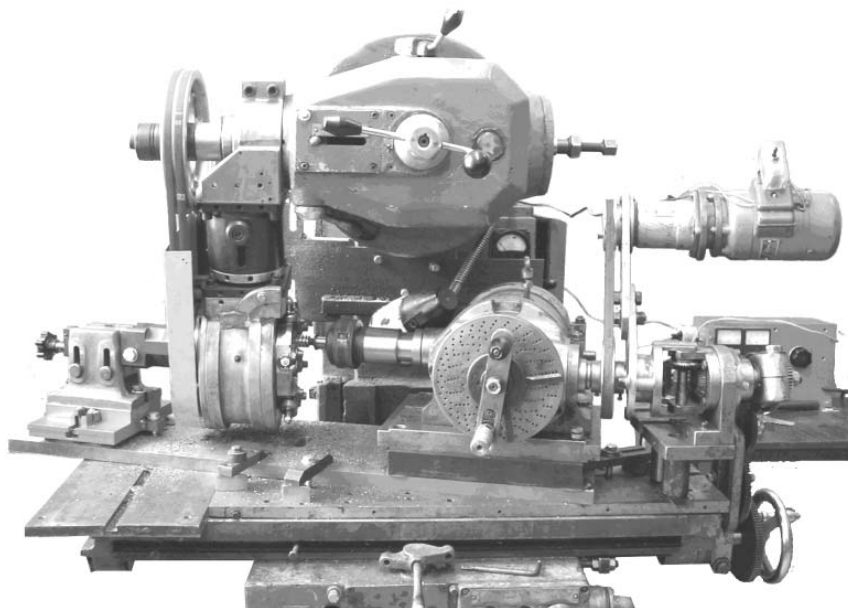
Модернізований вертикально-фрезерний верстат мод.6P10
